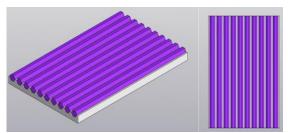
Зубчатая броня с врезанными элементами из высокопрочной стали
